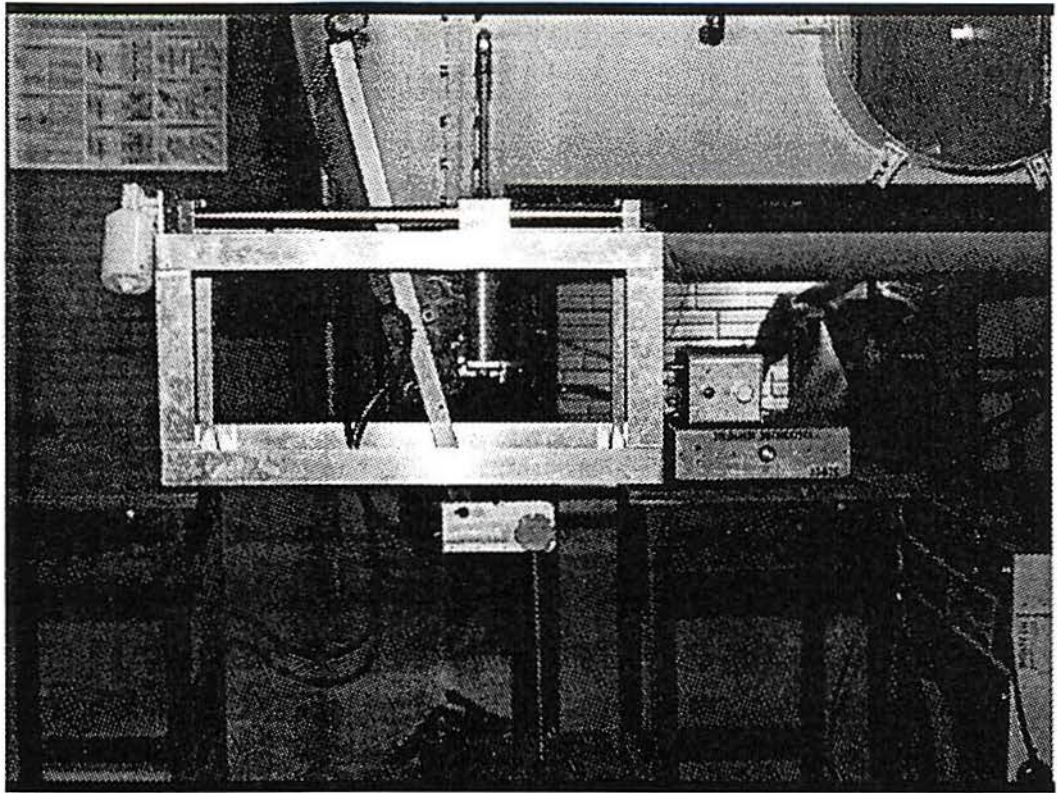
Dispositivo mecanizado de soldagem.
